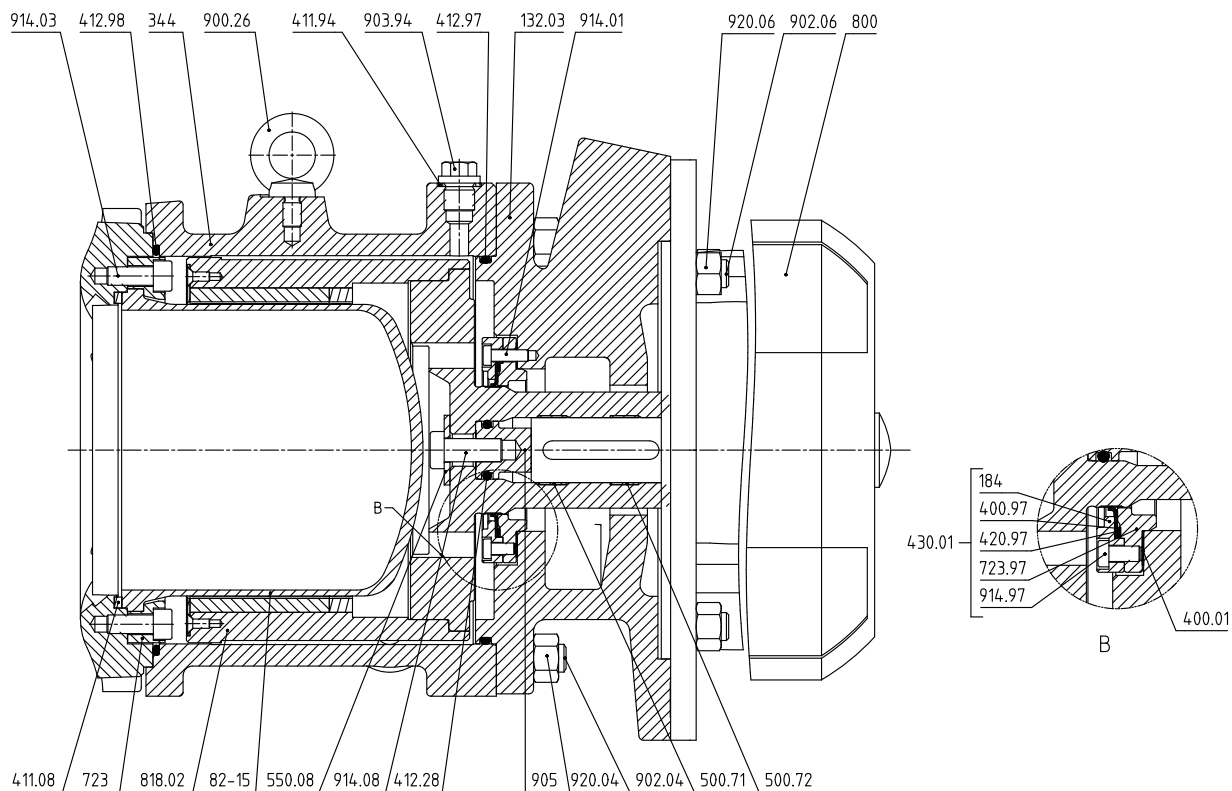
Ausführung mit keramischem Spalttopf und Leckagebarriere Wellendichtring
